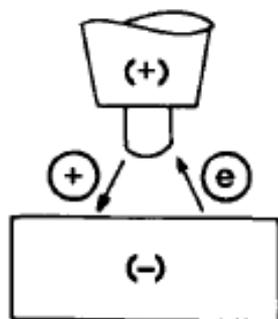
Soldagem TIG em corrente contínua de polaridade reversa<sup>(8)</sup>
